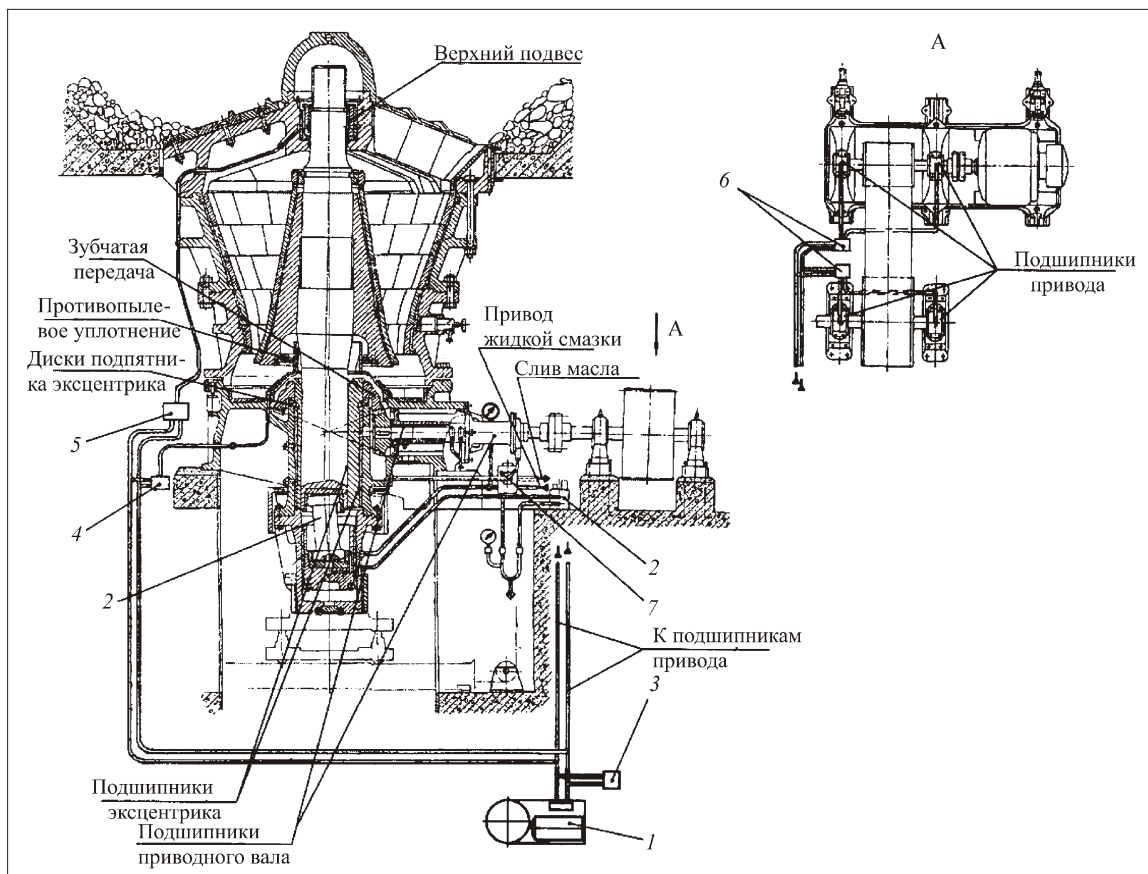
Разводка смазки по дробилке ККД-1500/180:
